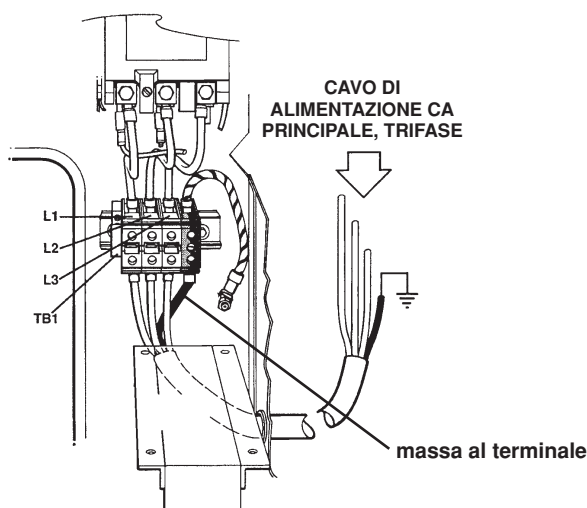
Collegamenti del cavo di alimentazione elettrica
